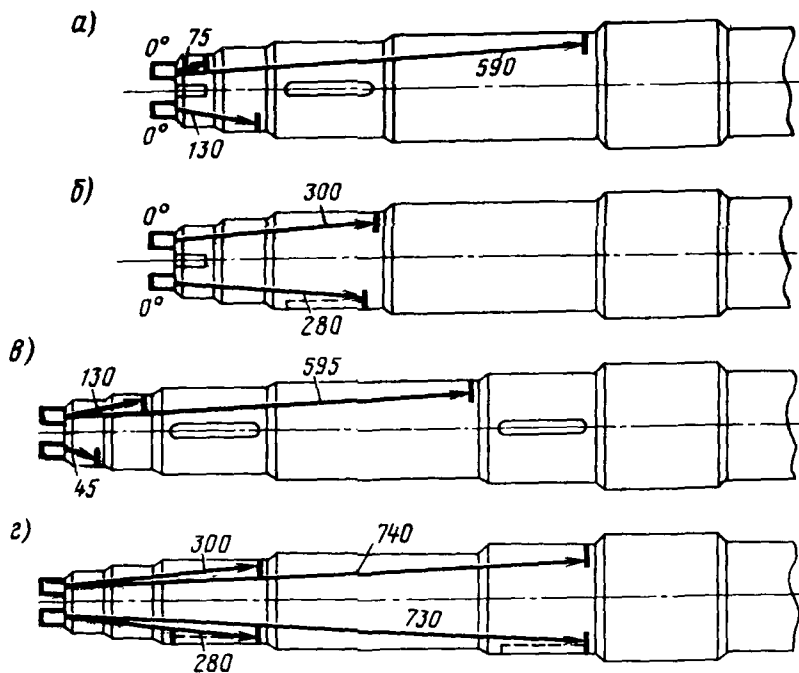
Схемы и зоны контроля прямым искателем со стороны торцов главного приводного вала эскалатора КДС при различном положении искателей (а, б, в, г)
